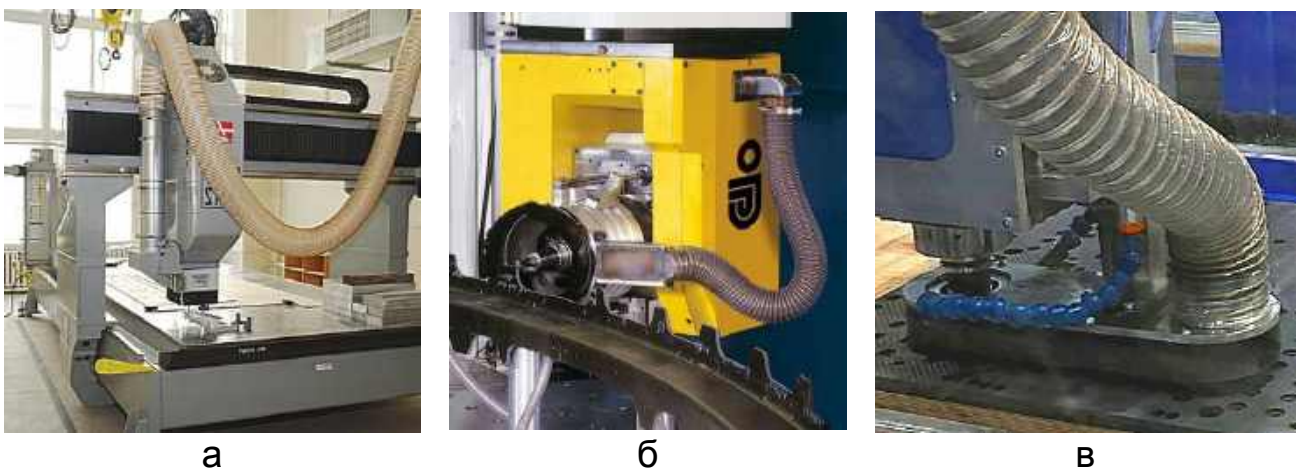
Загальний вигляд витяжної вентиляції на верстаті з ЧПК (а), приймача стружки та пилу із зони фрезерування (б) та свердління (в) КМ
